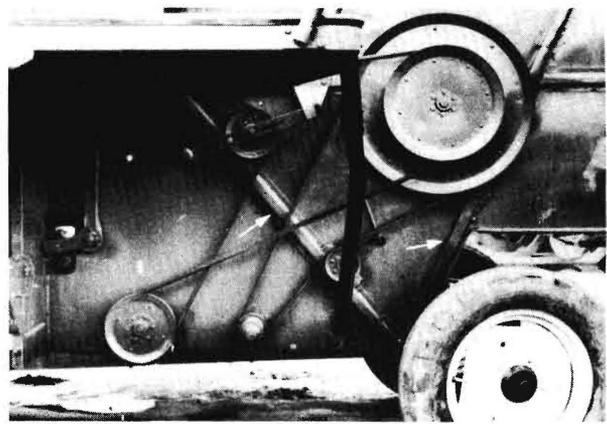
Formgepreßte Hutprofile, zur Verstärkung auf die Seitenwände des Maschinengehäuses aufgepunktet.
